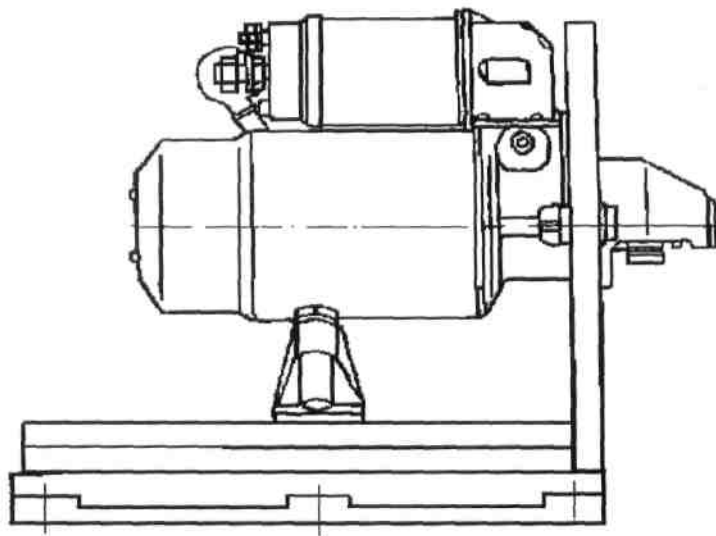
Установка стартера за фланец на столе нагрузочного устройства
